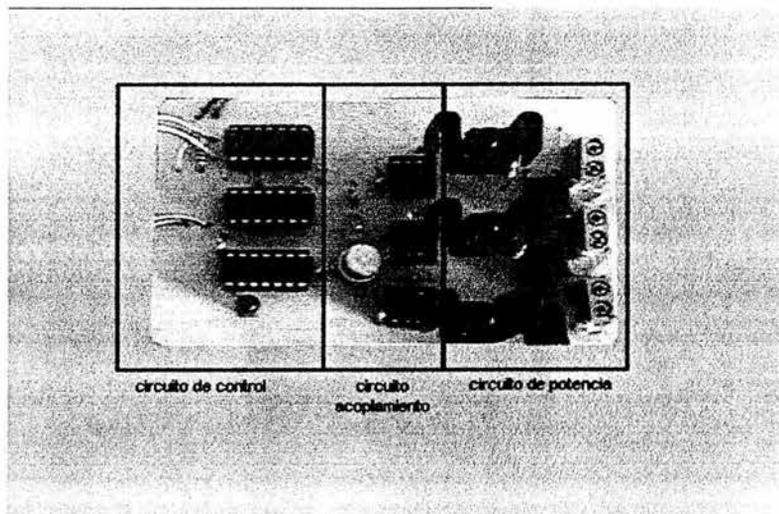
Etapas del circuito terminado y montaje de los componentes
